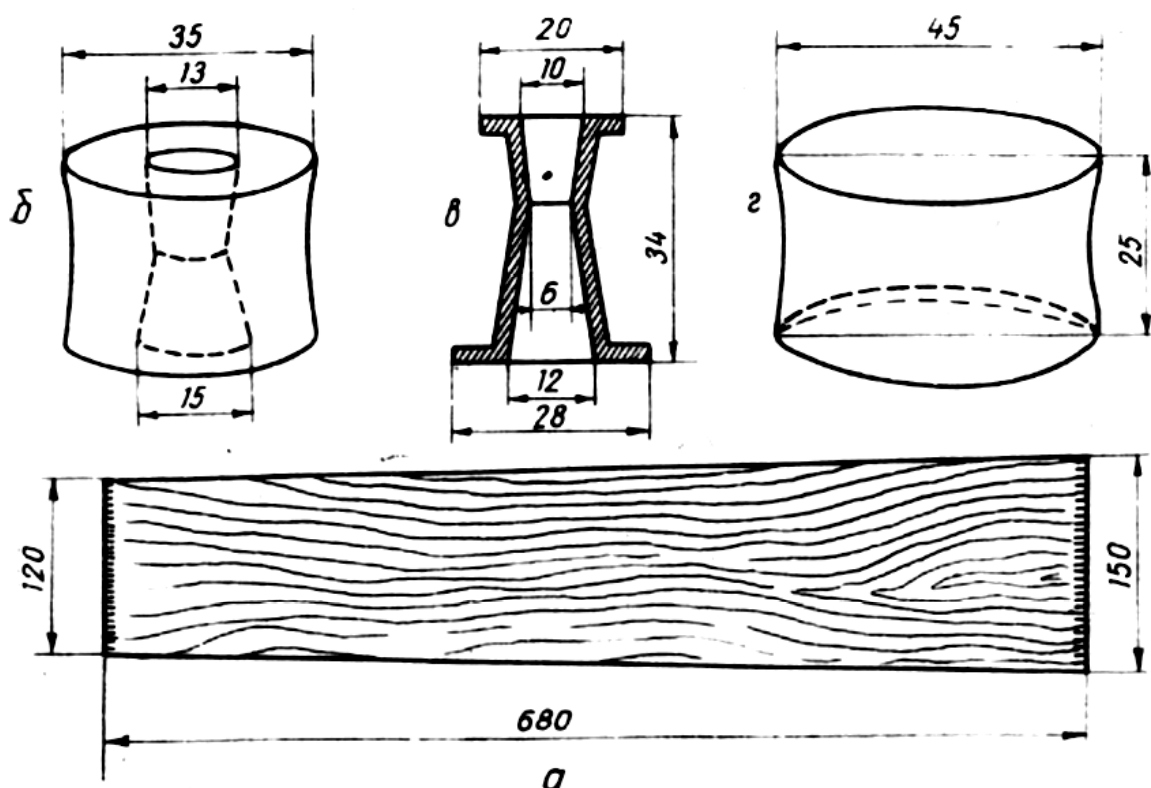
Деталі корпусу: а) заготовка з 1-мм дикту для стінок балона; б) нижня липова заглушка; в) дюралеве сопло в розрізі; г) верхня липова заглушка.
